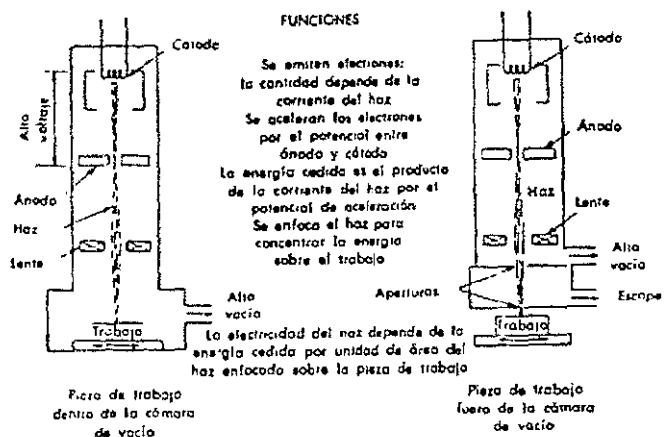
Diagrama esquemático de una operación de soldadura con haz electrónico
